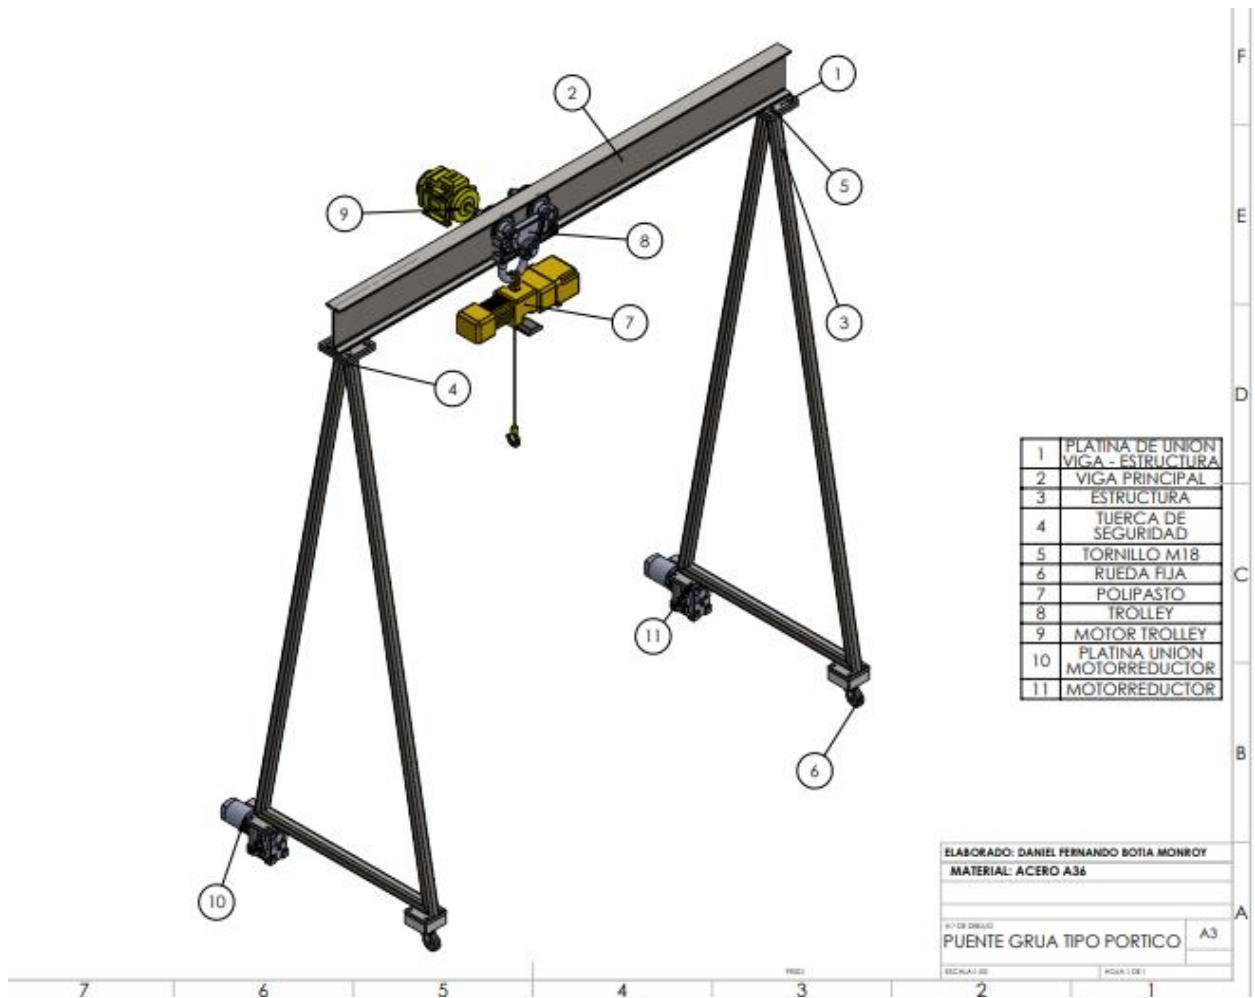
Diseño puente tipo pórtico. Fuente: Autor
